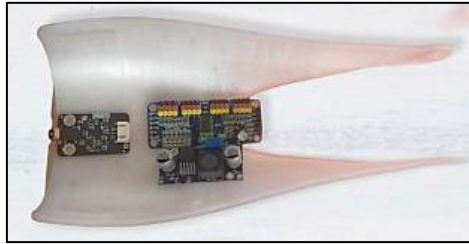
Montaje de Driver PWM 16. (Fuente: Autores)
